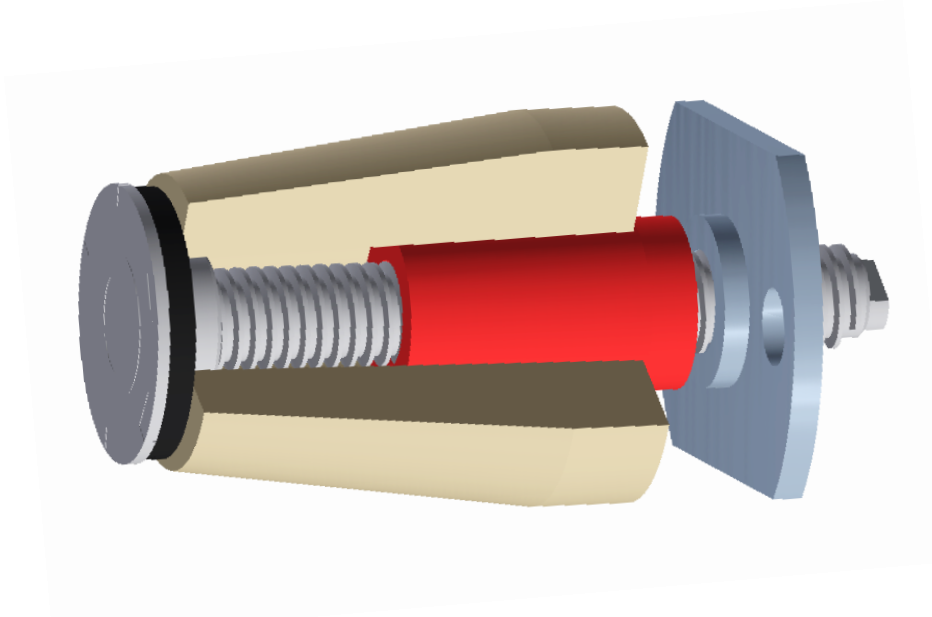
Nylon-Einbettwerkzeug mit konischer Hülse
